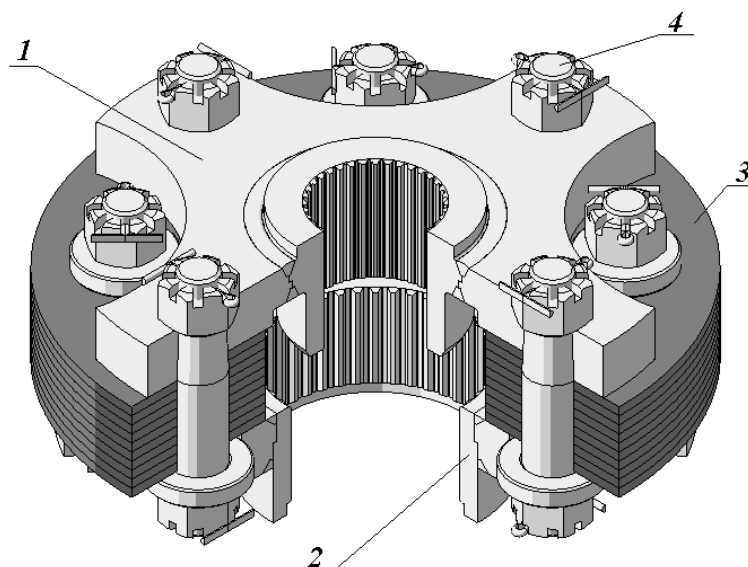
Шинно-зубчатая муфта: 1 – полумуфта; 2 – полумуфта; 3 – кольцо; 4 – палец
